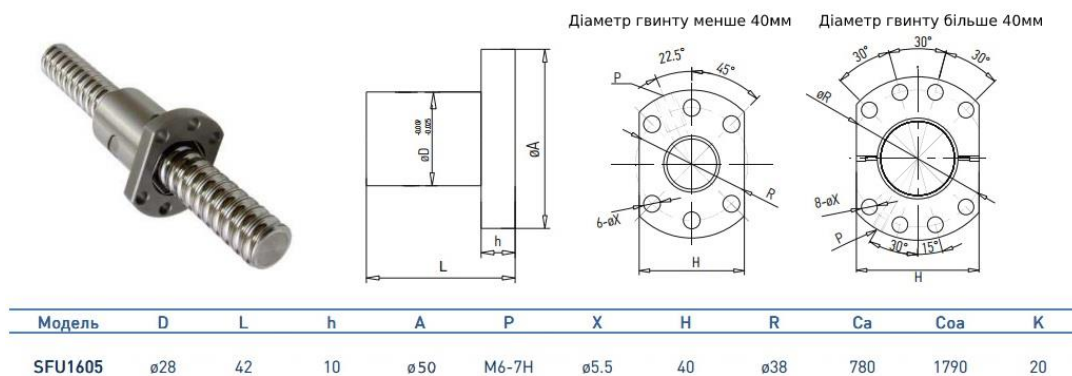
Креслення шарикової гайки рульового механізму
